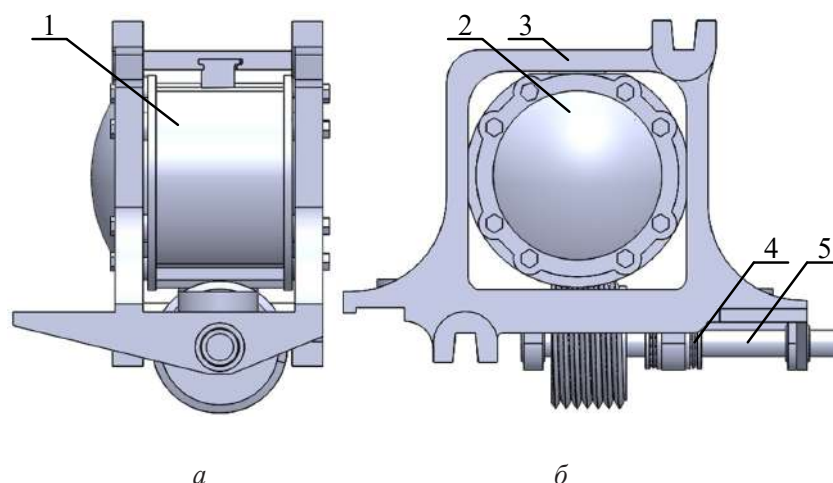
Новая конструкция буксового узла электровоза для механических систем РУКП: *а* — вид сбоку, *б* — вид спереди; 1 — корпус буксы, 2 — передняя крышка, 3 — рама буксы, 4 — упорный подшипник, 5 — винт
